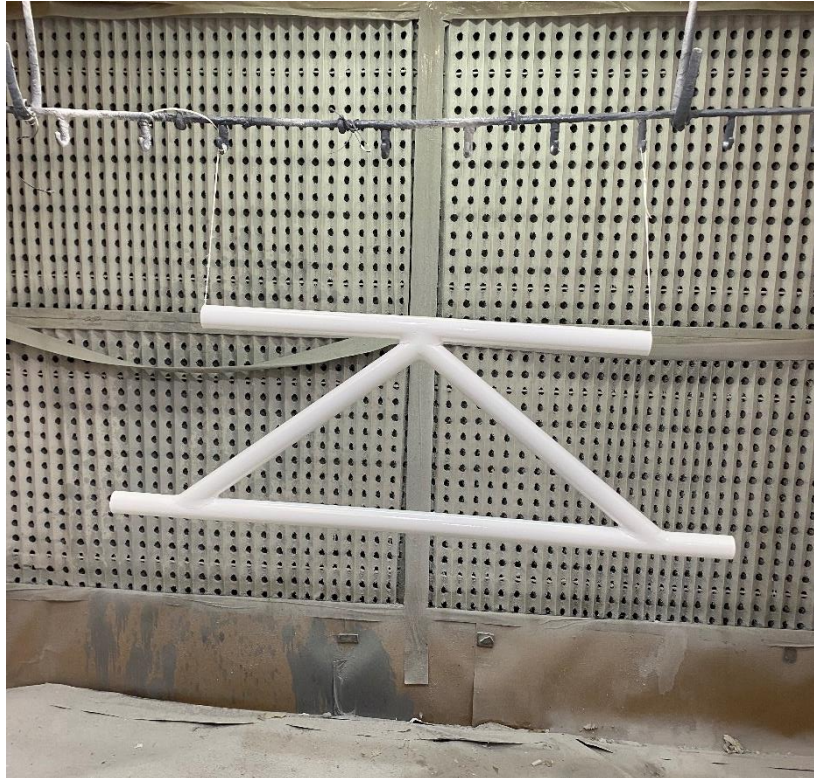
Pieza soldada por profesional (con certificado de soldadura). [Fuente propia]
